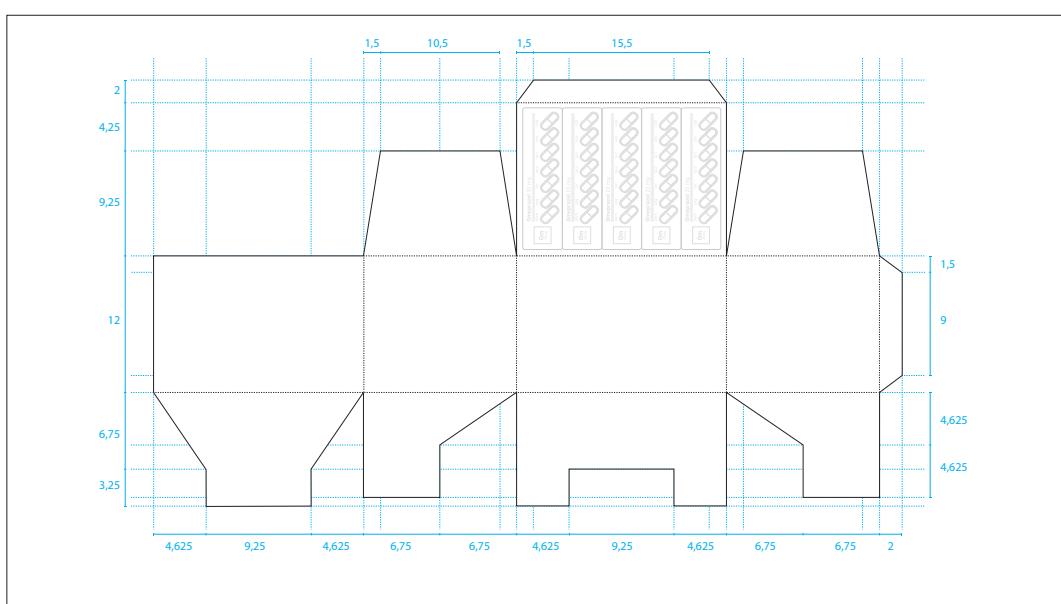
Planimetria da caixa de fornecimento do segundo blister menor (Padrão 2).
